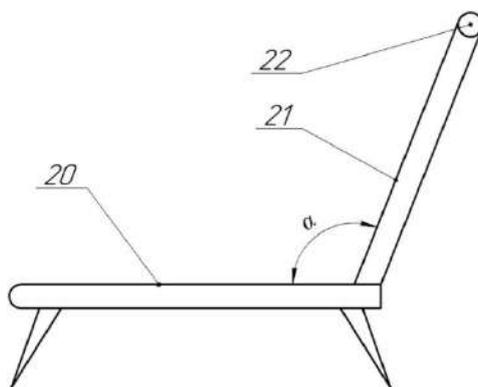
Подставка для сборщика хмеля (вид сбоку): 20 - подставка; 21 - упор; 22 - ручка; 23 - ножки; α – угол наклона упора к поверхности подставки
